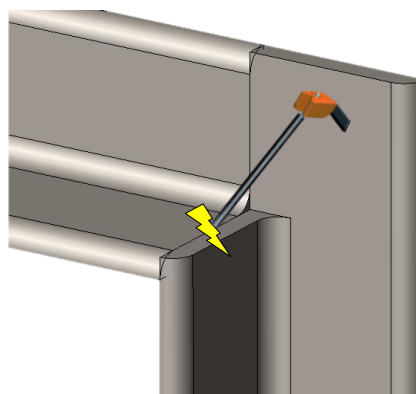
Verschweißen der Winkelzarge
